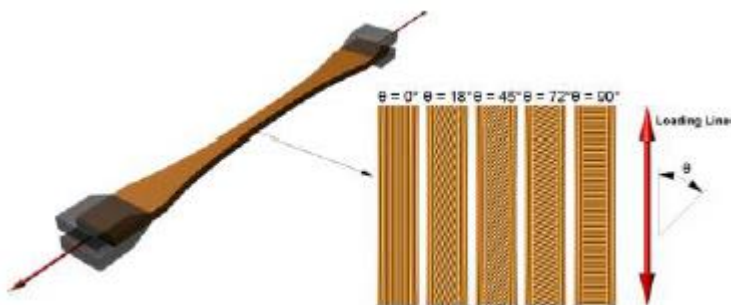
Orientazione del filamento rispetto a una direzione principale [15]
